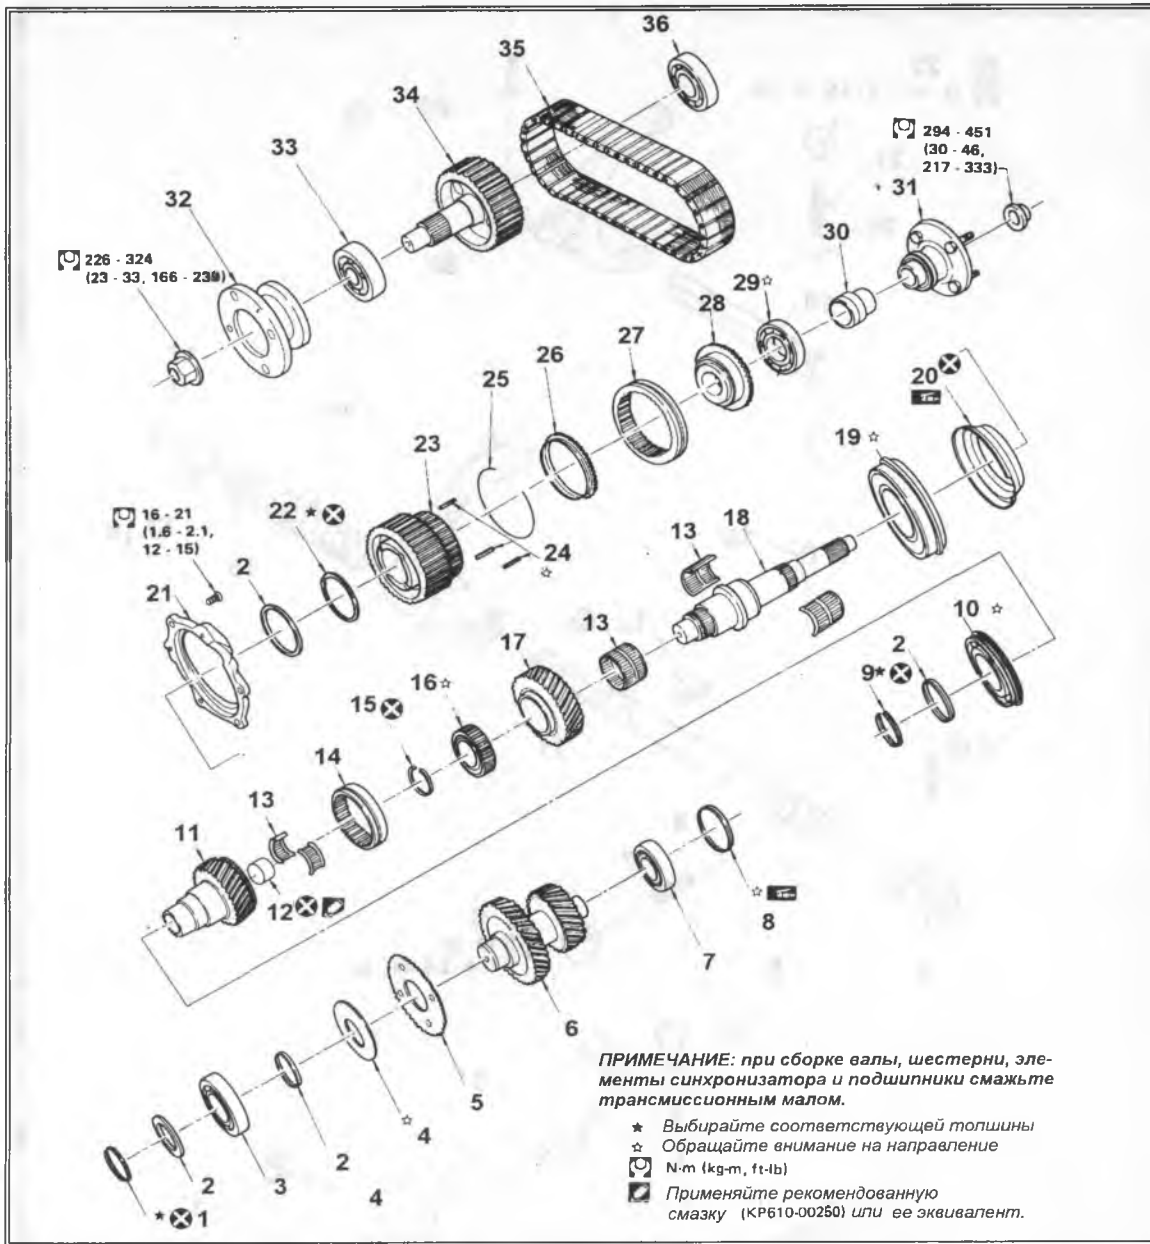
1. Пружинное стопорное кольцо. Повторно не используется. Подбирается по толщине. 2. Распорная шайба. 3. Передний подшипник промежуточной шестерни. 4. Тарельчатая пружина. 5 Накладная шестерня. 6. Промежуточная шестерня. 7. Задний подшипник промежуточной шестерни. 8. Шайба заднего подшипника промежуточной шестерни. При сборке обратите внимание на направление установки. 9. Пружинное стопорное кольцо. Повторно не используется. Подбирается по толщине. 10. Подшипник главной шестерни с пружинным стопорным кольцом. При сборке обратите внимание на направление установки. 11. Главная шестерня. 12. Втулка. Повторно не использовать. При сборке нанести слой герметика. 13. Игольчатый подшипник. 14. Подвижная муфта включения пониженной передачи. 15. Пружинное стопорное кольцо. Повторно не использовать. 16. Ступица механизма включения пониженной передачи. 17. Шестерня пониженной передачи. 18. Главный (вторичный) вал. 19. Передний подшипник главного вала с пружинным стопорным кольцом. При сборке обратите внимание на направление установки. 20. Маслоотражатель. Повторно не используется. При сборке смажьте кромки. 21. Держатель подшипника. Момент затяжки болтов крепления 1,6-2,1 кг-м. 22. Пружинное стопорное кольцо. Повторно не используется. Подбирается по толщине. 23. Шестерня переднего привода. 24. Подвижные вкладыши. При сборке обратите внимание на направление установки. 25. Распорная пружина. 26. Блокирующее кольцо. 27. Подвижная муфта переключения привода (2WD-4WD). 28. Механизм сцепления. 29. Задний подшипник главного вала. Обратите внимание на направление установки. 30. Шестерня привода спидометра. 31. Задний фланец. Момент затяжки гаек крепления 30-46 кг-м. 32. Передний фланец. Момент затяжки гаек крепления 23-33 кг-м. 33. Передний подшипник вала переднего привода. 34. Вал переднего привода. 35. Цепь привода. 36. Задний подшипник вала переднего привода.
